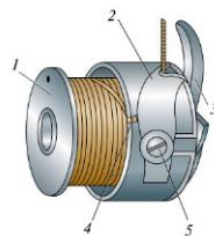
Устройство шпульного колпачка: 1 – шпулька; 2 – пластинчатая пружина; 3 – установочный палец; 4 – косая прорезь; 5 – регулировочный винт
